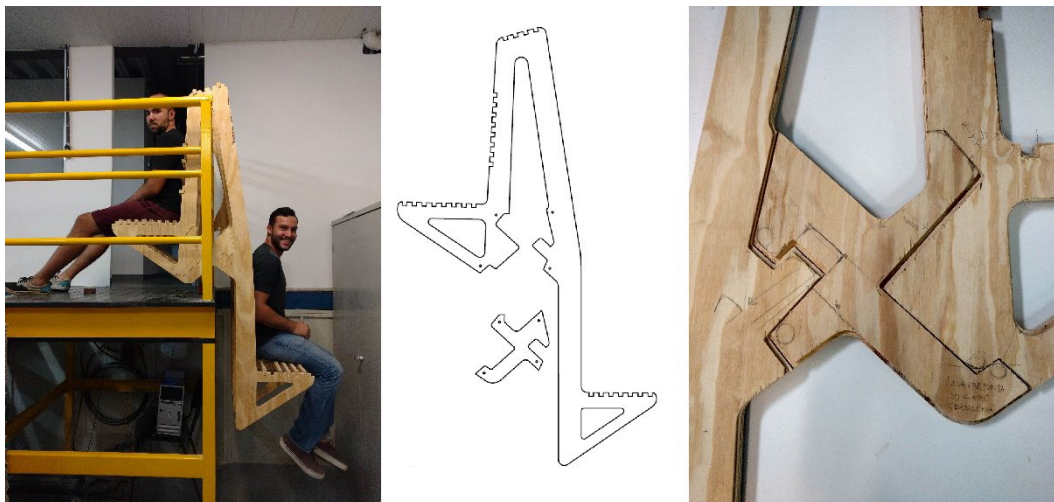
Banco da Banca, detalhe construtivo do Septo
